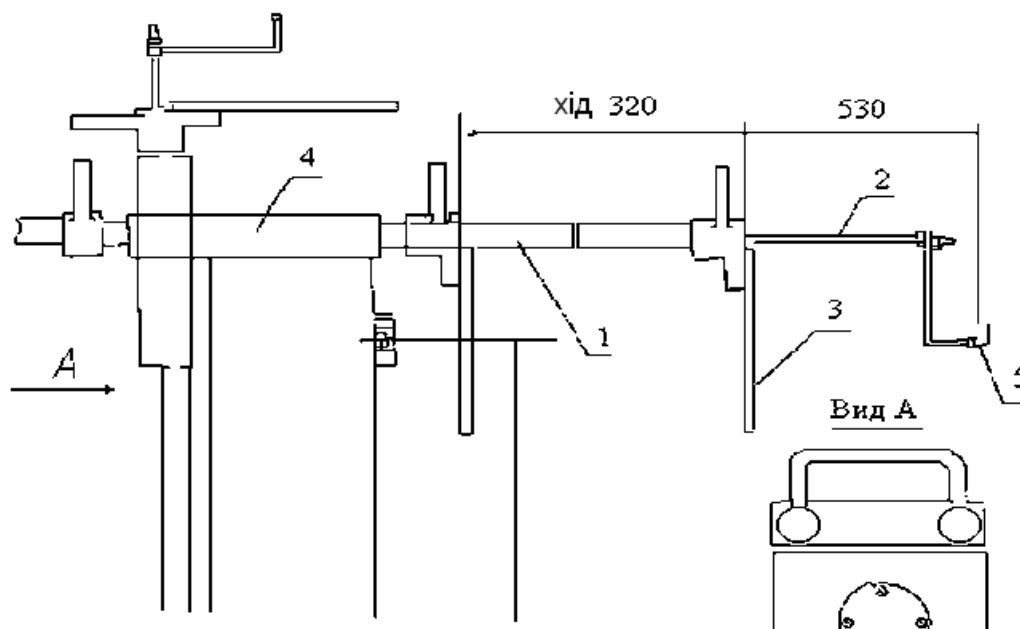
Стійка з полозками: 1 – полозки; 2 – лінійка-щуп; 3 – шкала; 4 – стійка; 5 – упор
